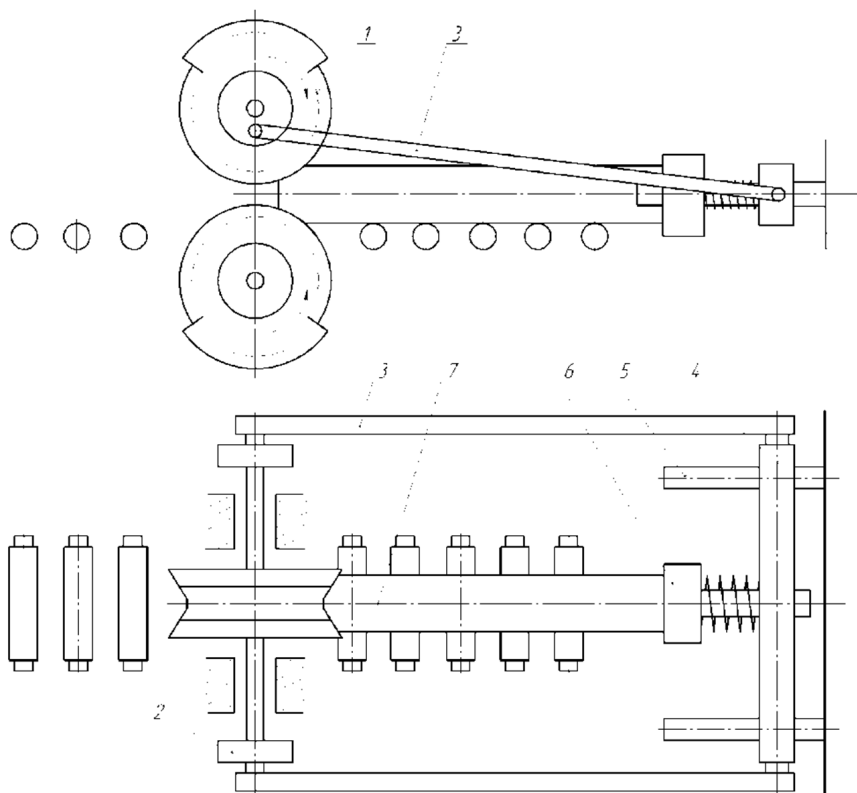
Схема стана 2198 для вальцовки заготовки передней балки
